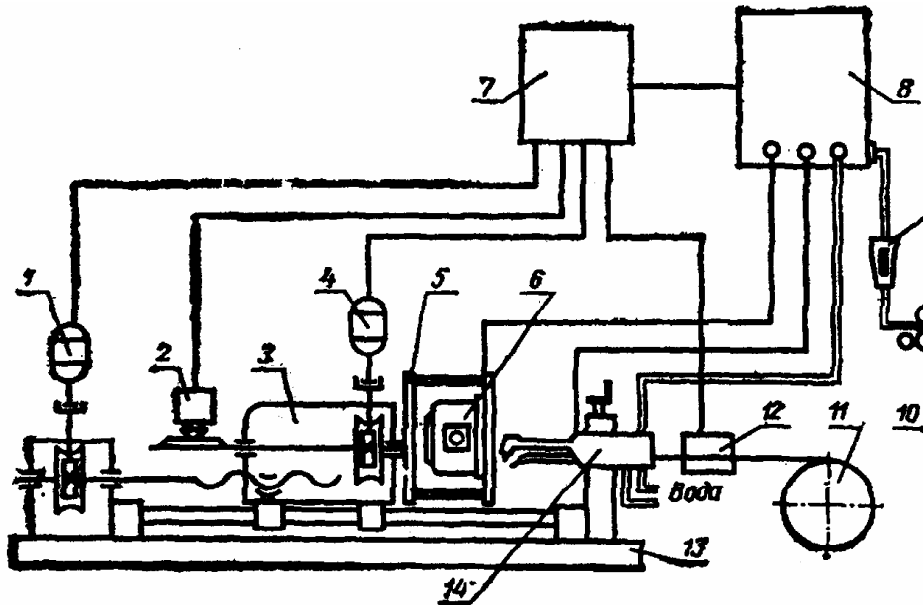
Принципова схема установки для автоматичного наплавлення корпусу шестеренного насоса НШ:
